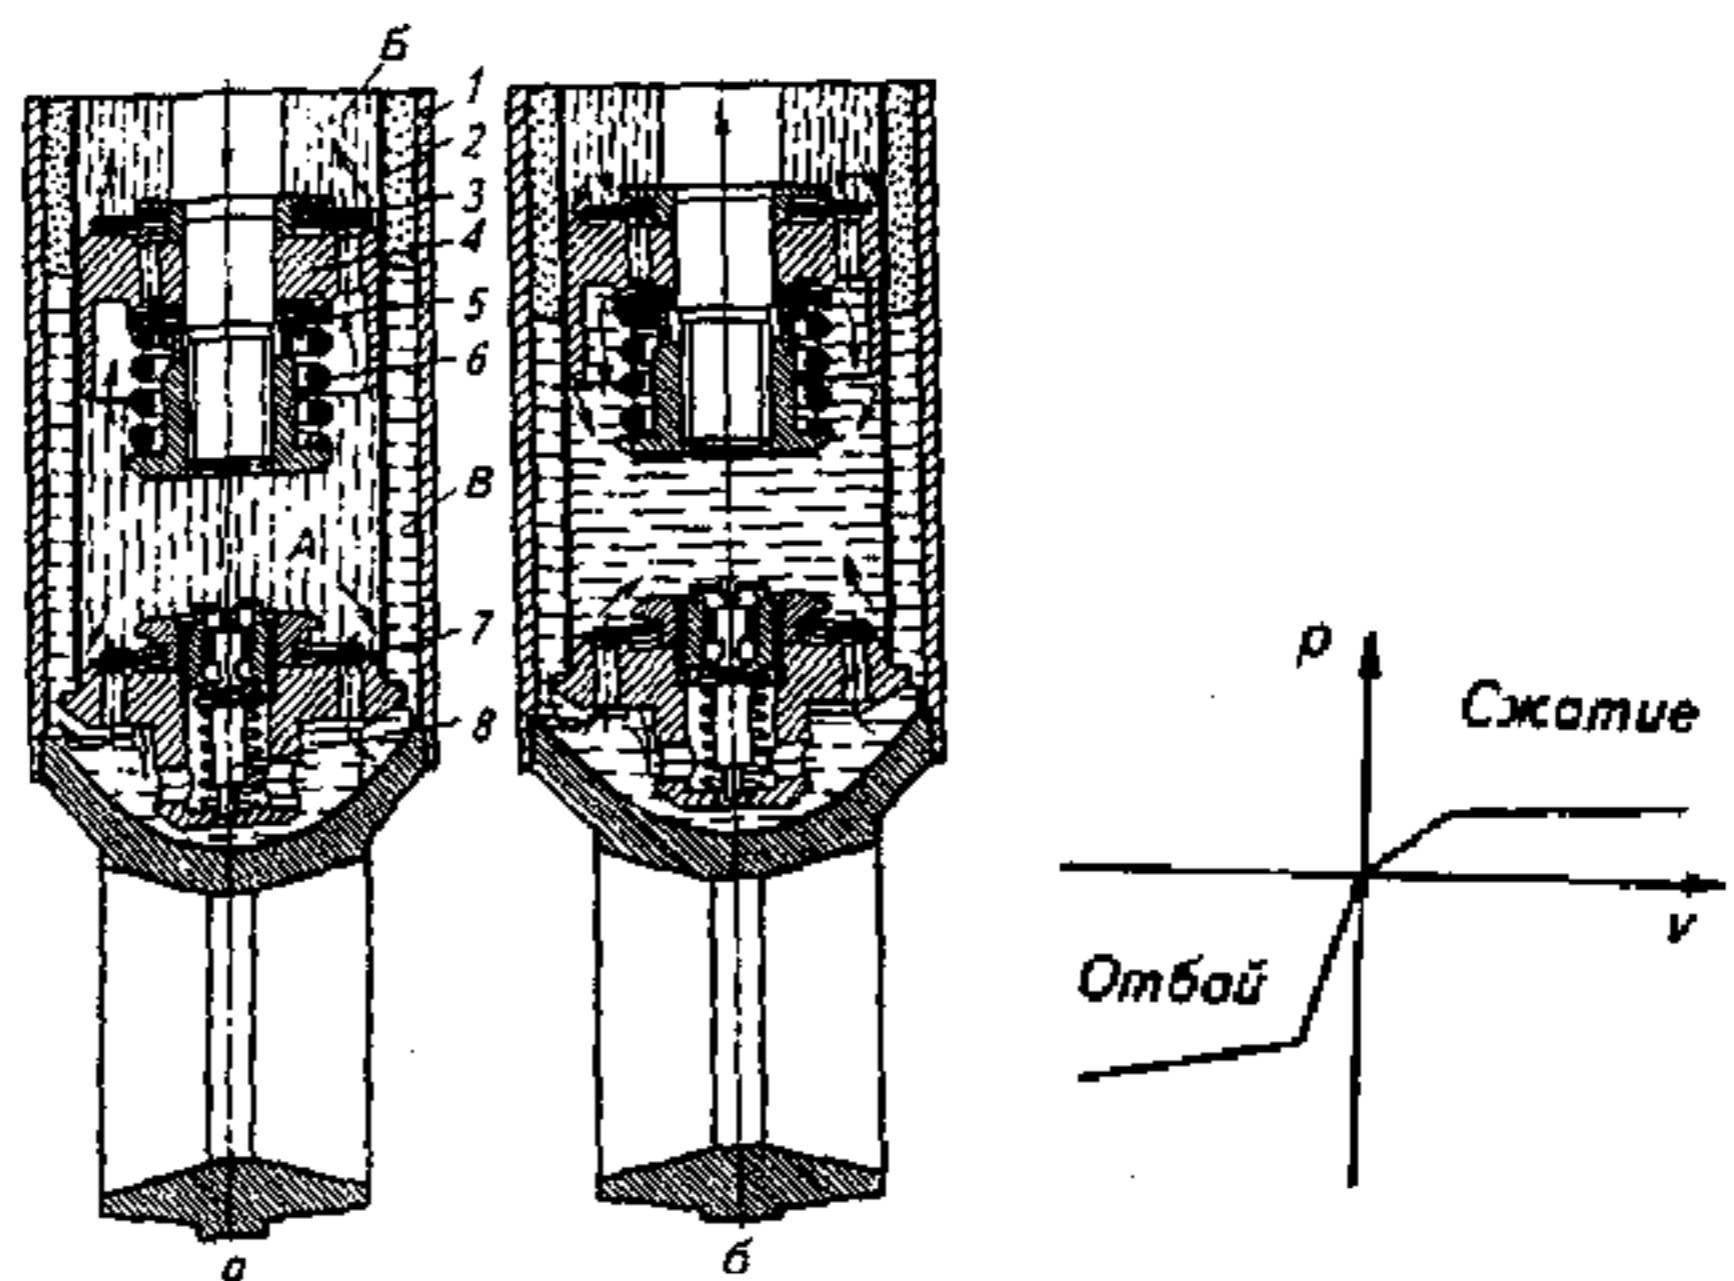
Схема работы амортизатора: *a* – сжатие рессоры; *б* – отбой рессоры; в – характеристики амортизатора; *A*, *B*, *В* – полости; 1 – рабочий цилиндр; 2 – корпус резервуара; 3 – перепускной клапан; 4 – поршень; 5 – клапан отбоя; 6 – пружина; 7 – всасывающий клапан; 8 – разгрузочный клапан
